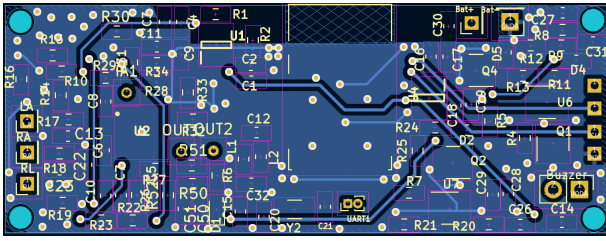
Diseño de la capa superior del PCB. Fuente: Elaboración propia.
